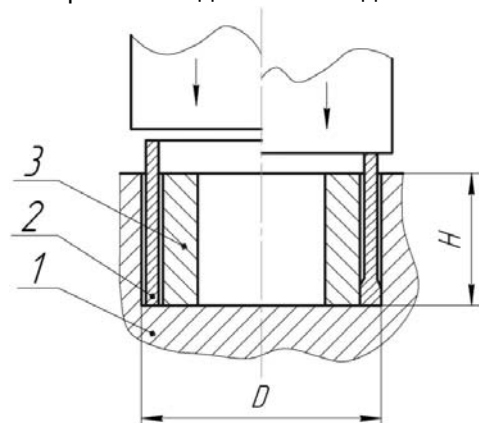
Прессовое соединение, содержащее пластически деформируемую промежуточную втулку
